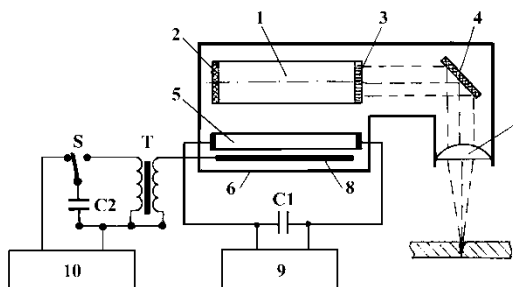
Схема сварочной установки с твердотельным лазером:
